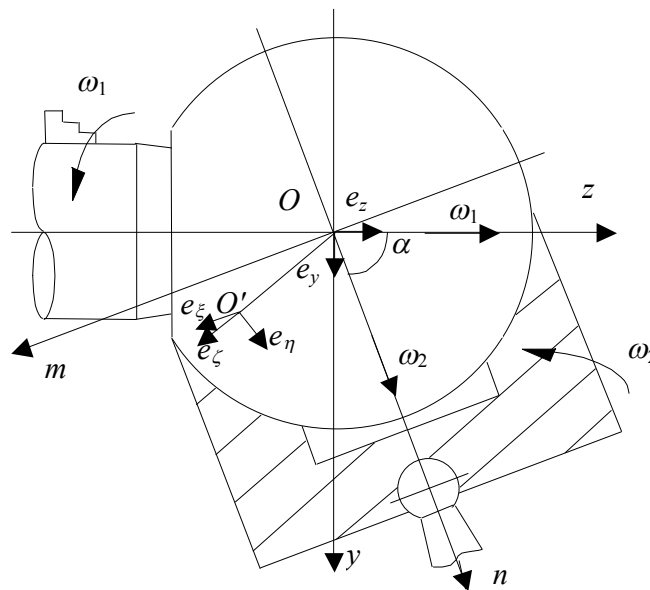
Схема алмазно-абразивного доведення деталі кульпоподібної форми
